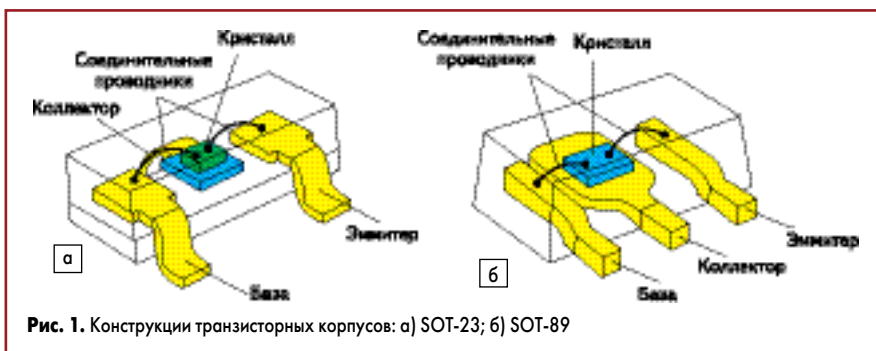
Конструкции транзисторных корпусов: а) SOT-23; б) SOT-89
